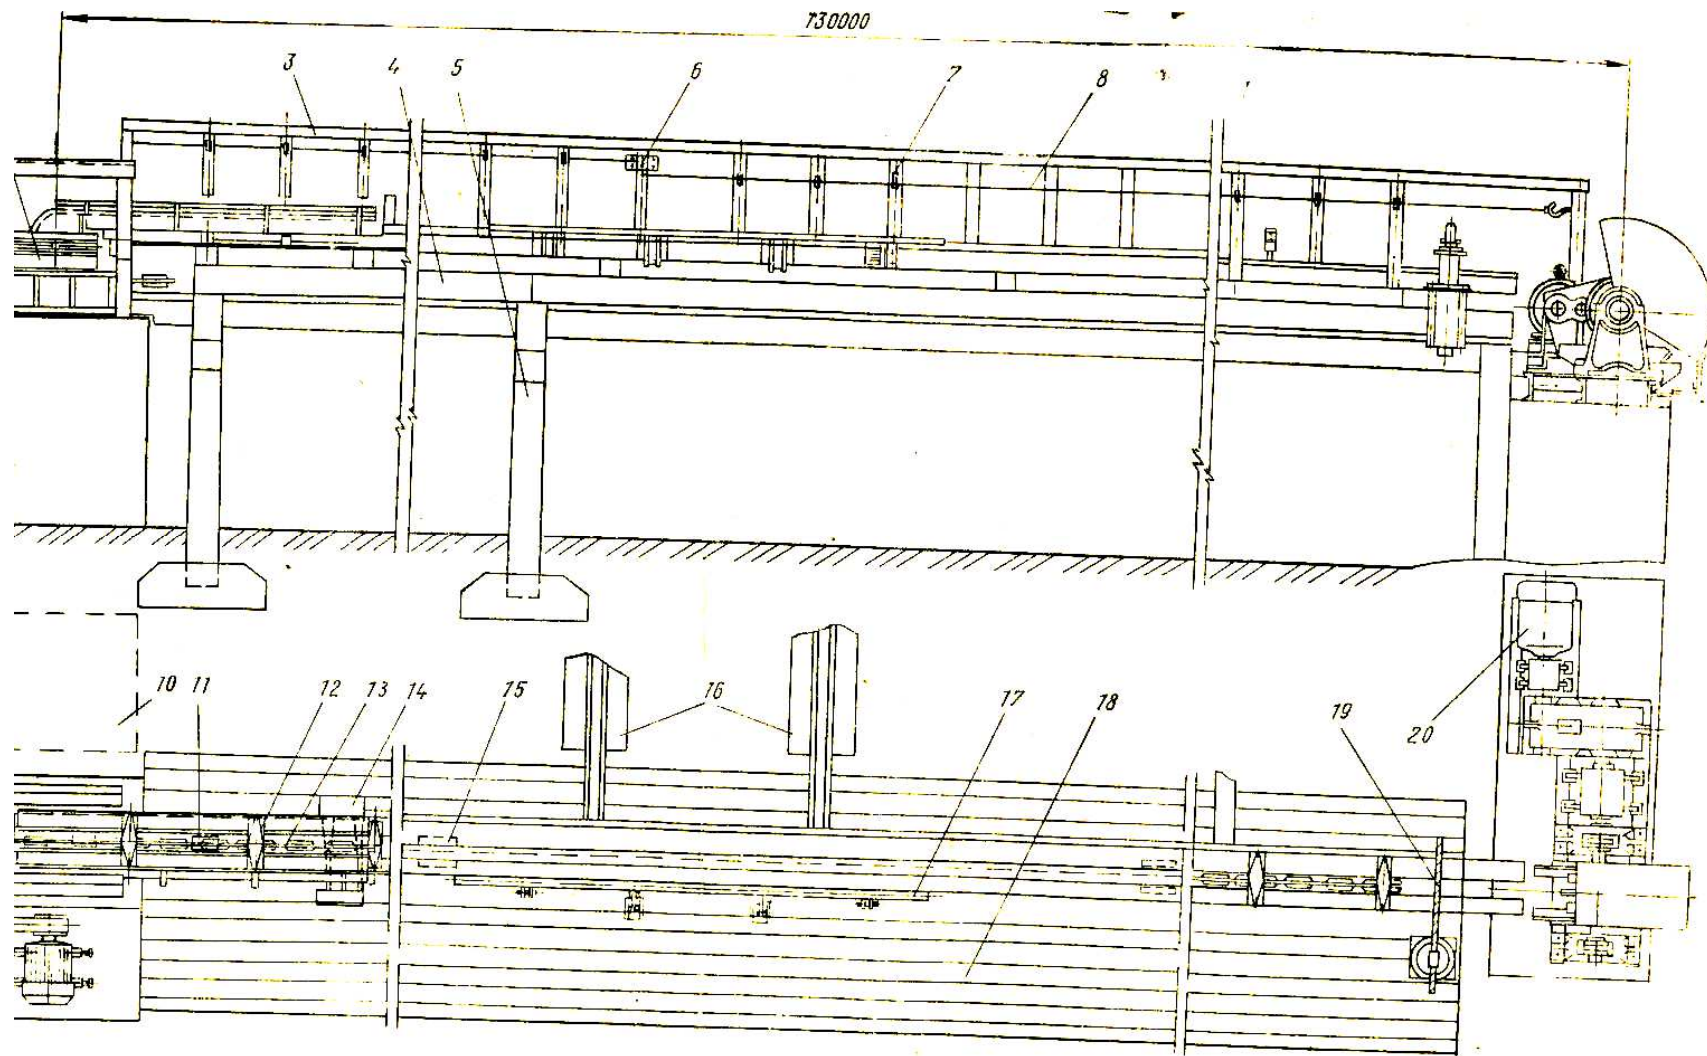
Общий вид лесотранспортера ЛТ-86А
